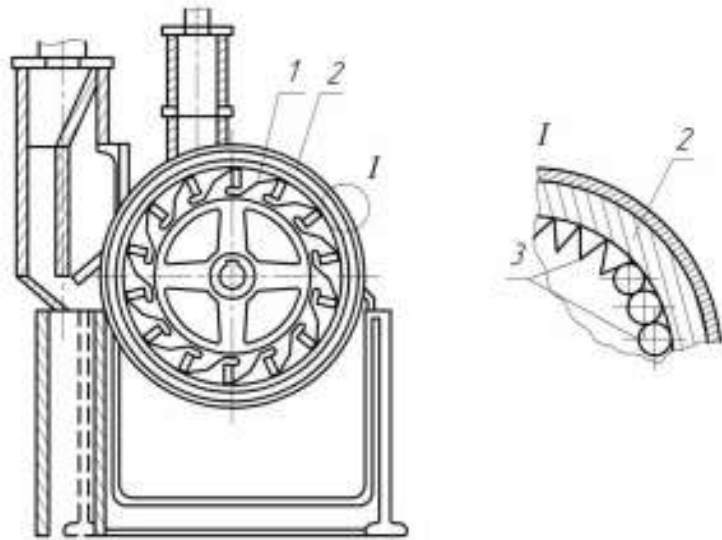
Бильна машина зі сталевими билами і циліндром
